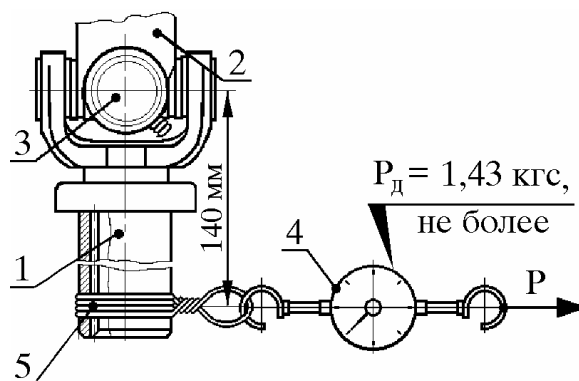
Проверка момента поворота в шарнире карданного вала и скользящей вилки:
